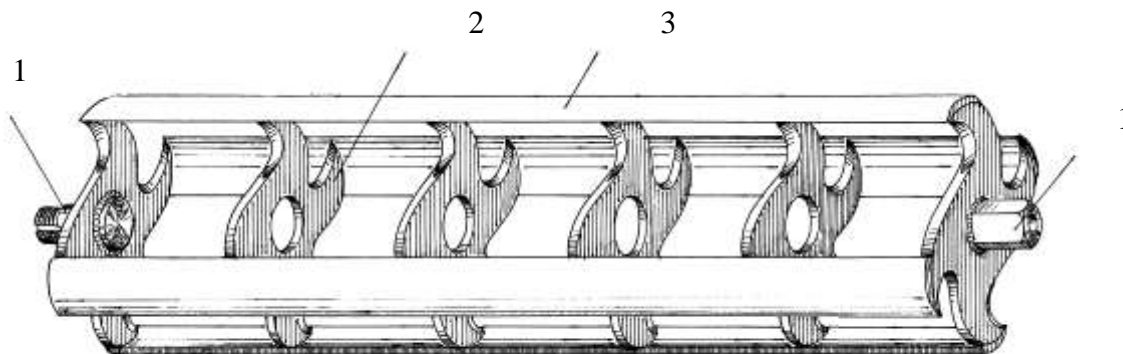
Фрезерный рабочий орган «безвального типа»: 1 – цапфы; 2 – фреза; 3 – горизонтальный нож.
